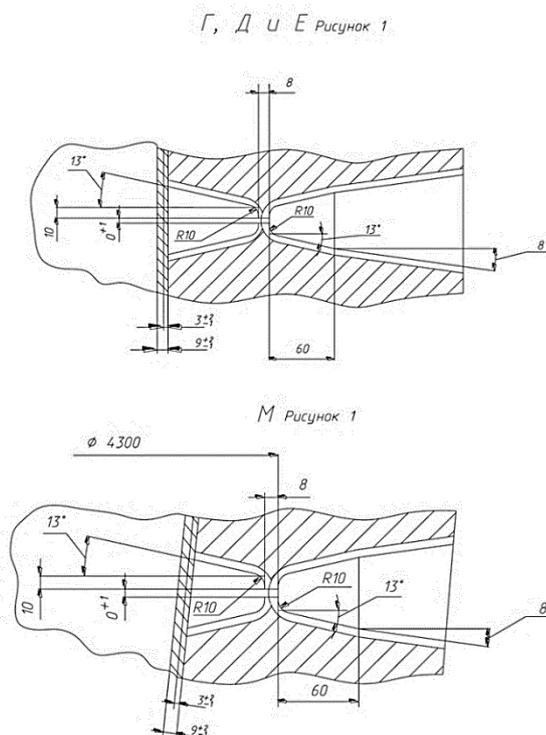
Сварные соединения обечаек корпуса реактора ВВЭР-1200
